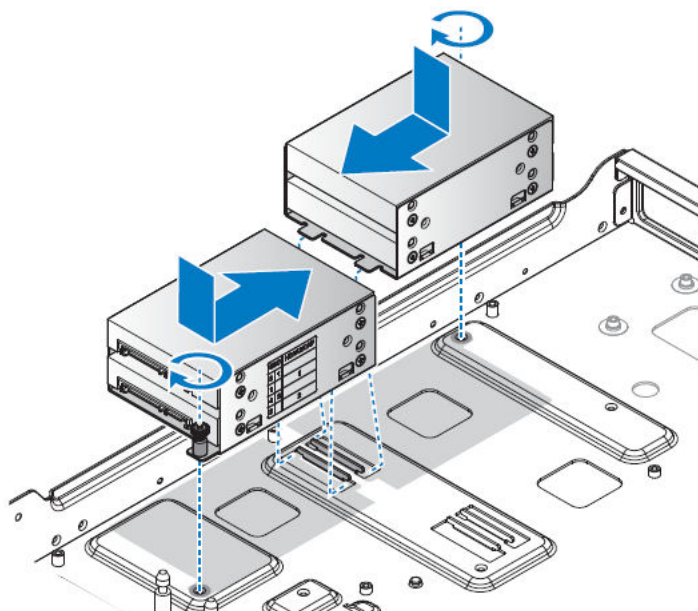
Installation de l'assemblage de disque dur de 2,5 pouces
